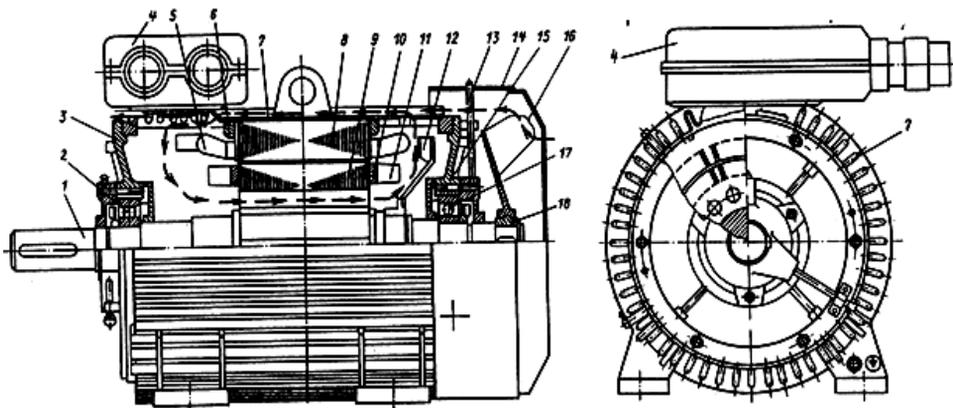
Асинхронный двигатель серии АИР112М4 -5,5кВт/ 1500 об/мин с короткозамкнутым ротором [1]: 1 – вал; 2, 17 – подшипники качения; 3, 15 – подшипниковые щиты; 4 – коробка выводов; 5 – лобовые части обмотки статора; 6 – нажимное кольцо статора; 7 – гофрированная станина; 8 – сердечник статора; 9 – сердечник ротора; 10 – 11 – вентиляционные лопасти; 12 – внутренний вентилятор; 13 – масленка для смазки подшипника; 14 – кожух вентилятора; 16 – наружный вентилятор; 18 – тулка вентилятора (стрелками показаны направления потоков охлаждающего воздуха)
